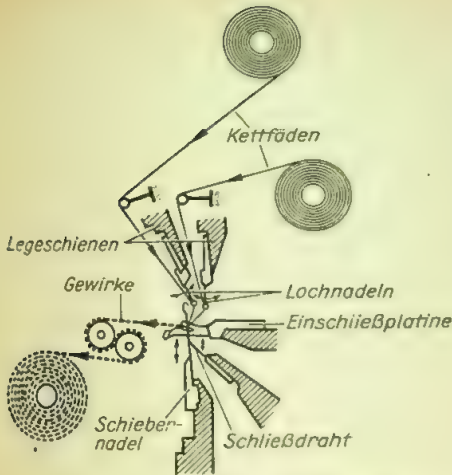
Prinzip einer Kettenwirkmaschine
